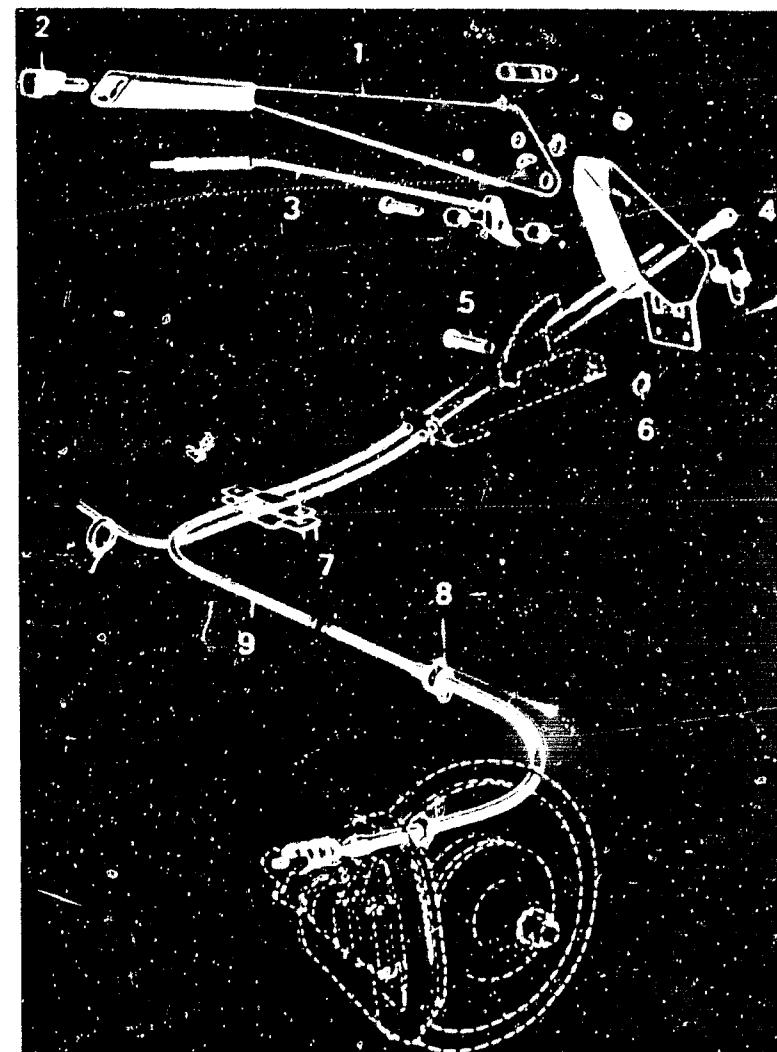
Handbremsbetätigung 1 Handbremshebel – 2 Druckknopf – 3 Sperrstange – 4 Einstellmutter – 5 Achsbolzen – 6 Sicherungsring – 7 Seilzughalter – 8 Radkastendurchführung – 9 Handbremsseilzug.
